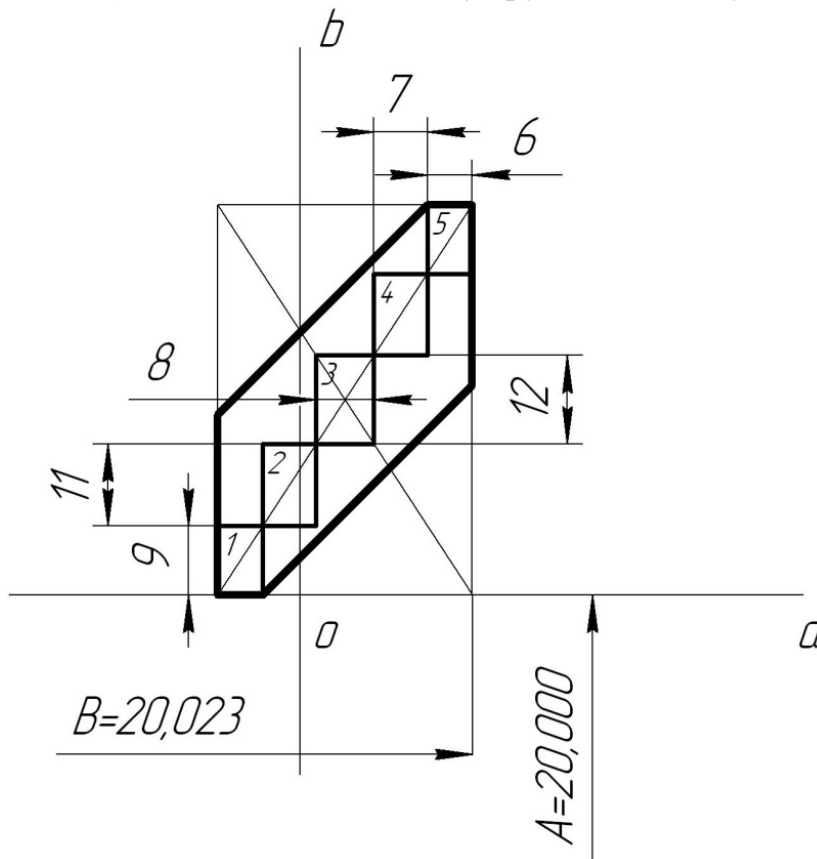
Разбиение многоугольника допусков на прямоугольники
